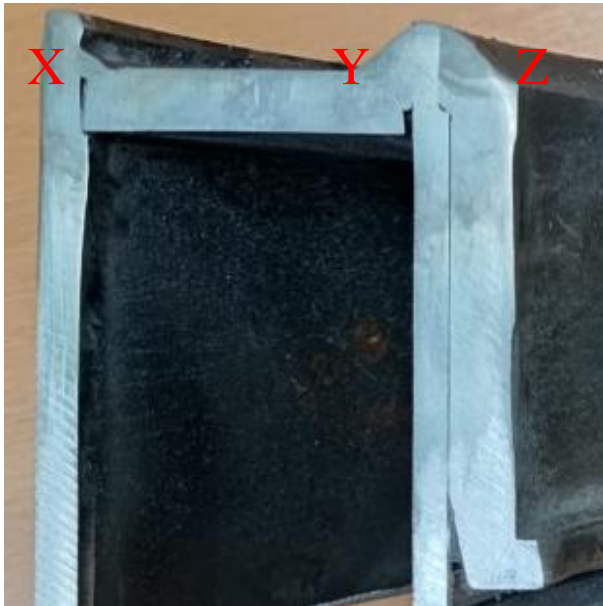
corpo de prova 4 Solda X, Y e Z.
